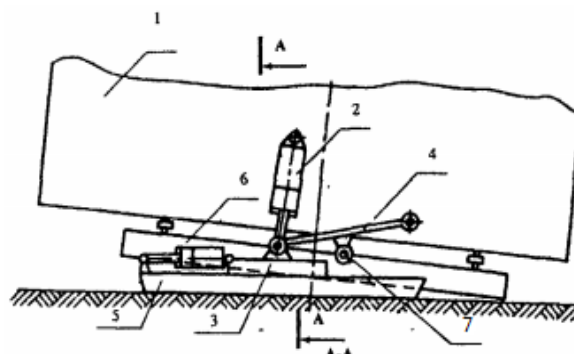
Схема трёхопорного механизма шагания с неполным отрывом базы:
